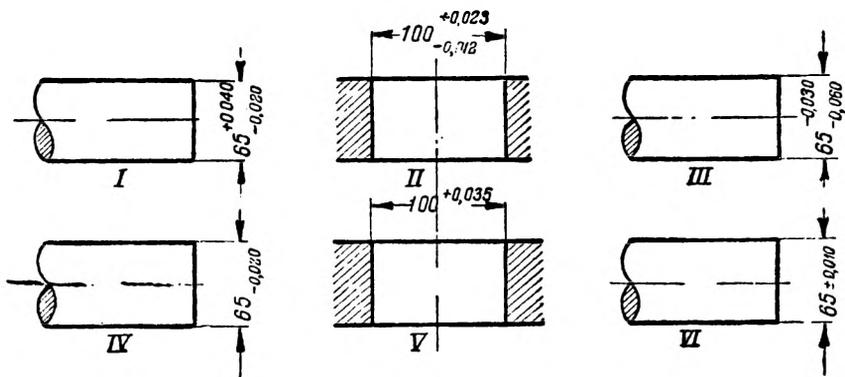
Номинальный, наибольший и наименьший размеры вала.
